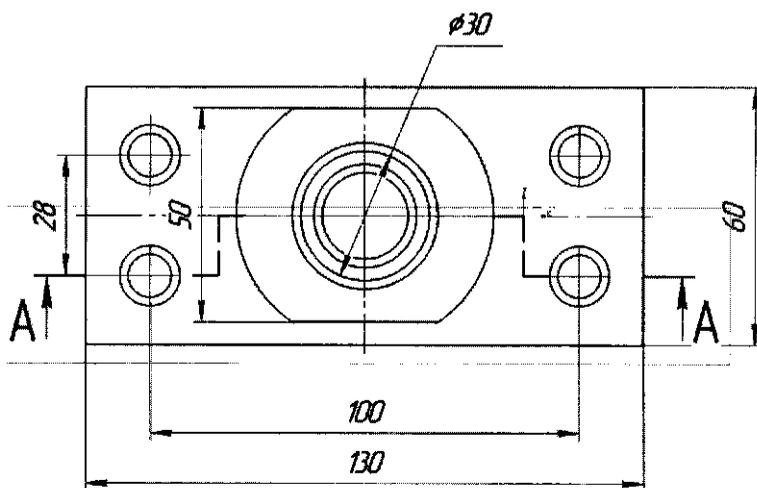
Конечный вид чертежа (вид сверху) с размерными линиями
